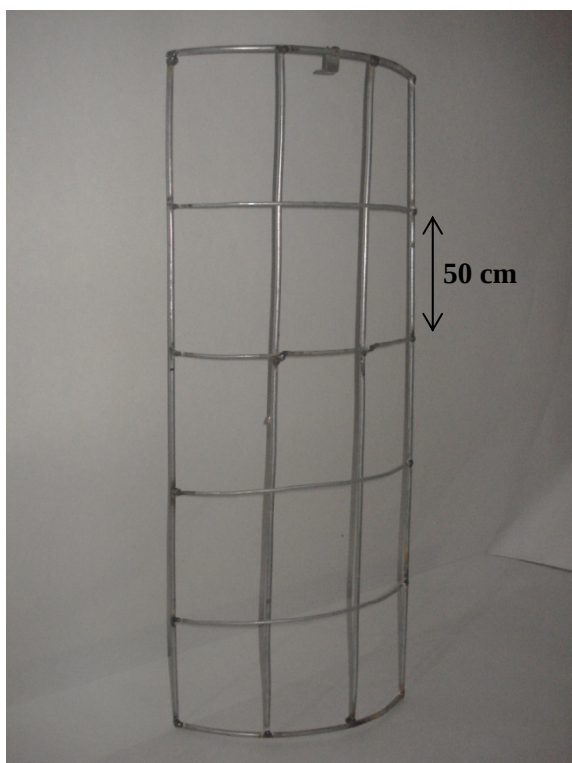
pieza soldada con elemento de sujeción de techo.
